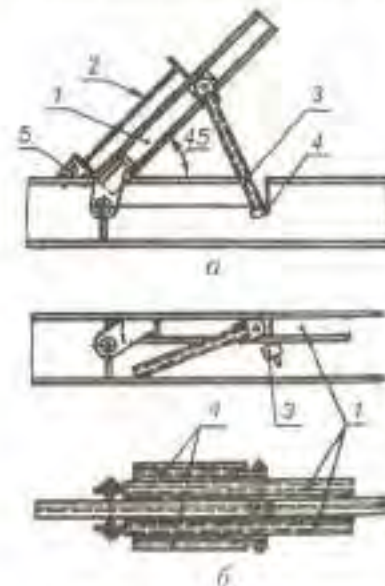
Пристрій для встановлення балок під зварювання:
